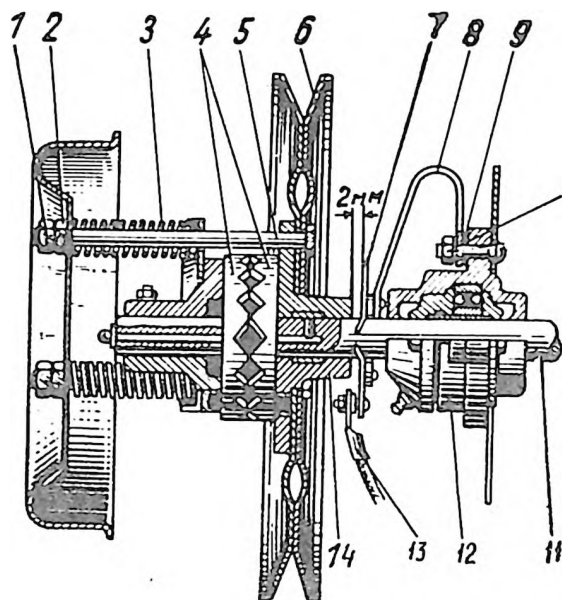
Регулировка предохранительной муфты шнека зернового элеватора: 5 - стягивающий болт; 6 - шкив шнека; 7 - электроконтакт; 8 - кронштейн; 9 - регулировочная шайба; 10 - гайка болта крепления кронштейна; 11 - вал шнека; 12 - корпус подшипника; 13 - провод контрольной лампочки; 14 - ступица шкива
